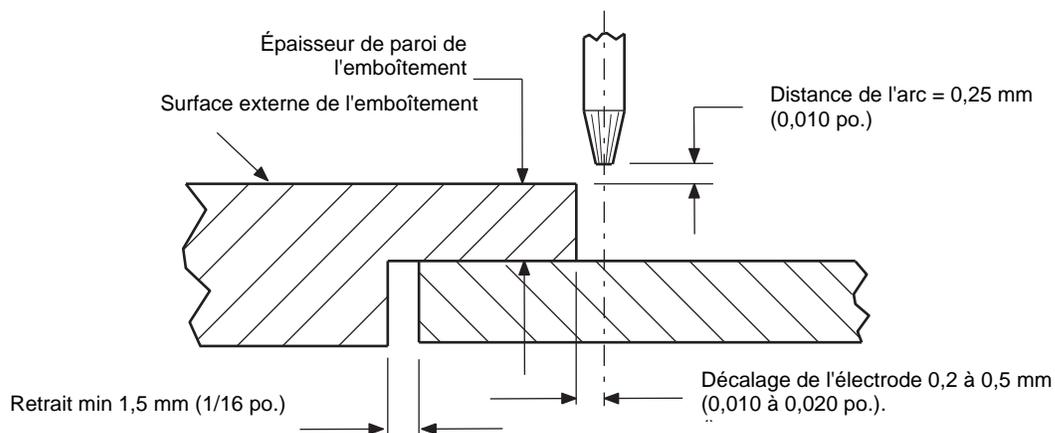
Distance de l'arc de la soudure par emboîtement
